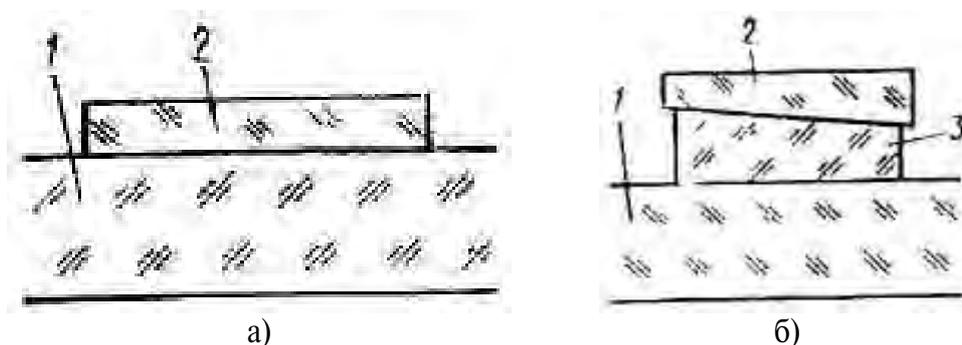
Крепление заготовок с помощью оптического контакта:
